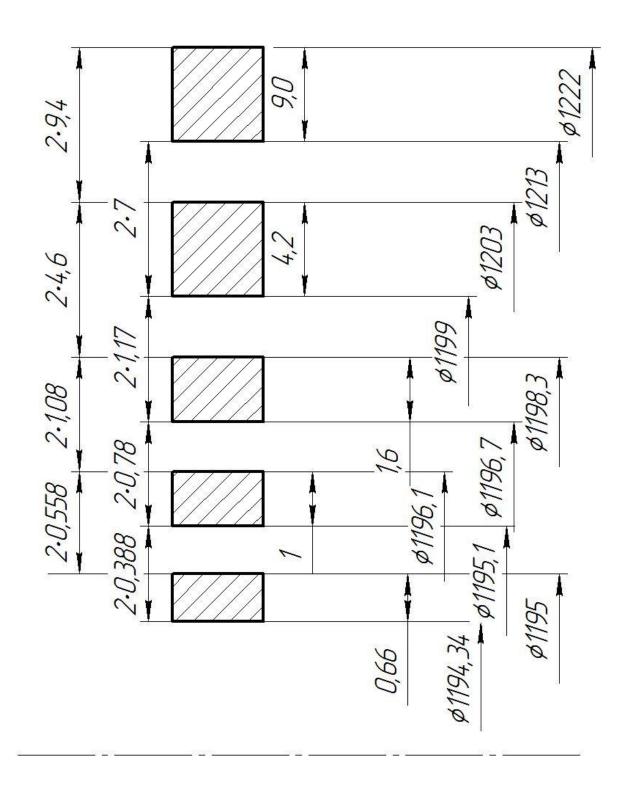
Схема припусков и допусков на обработку поверхности диаметром 1195h11(-0,66)
